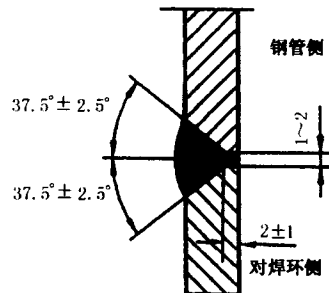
对焊环与钢管连接的焊接接头型式
